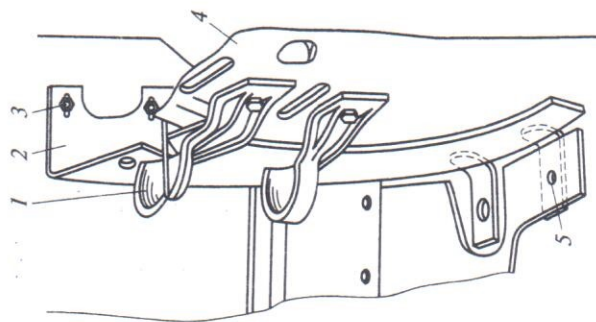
Регулировка положения боковины картофелесажалки:
